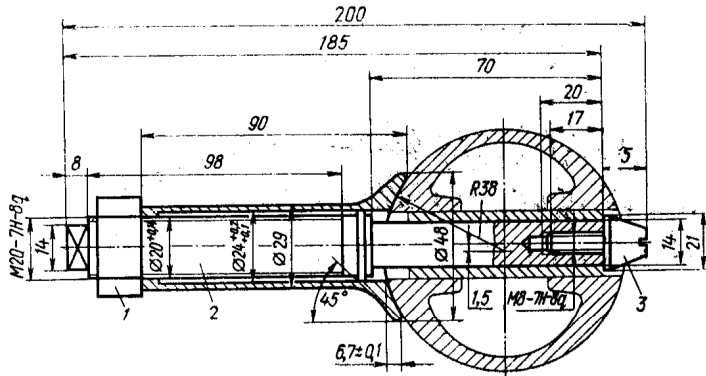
Приспособление для выпрессовки поршневого пальца:
